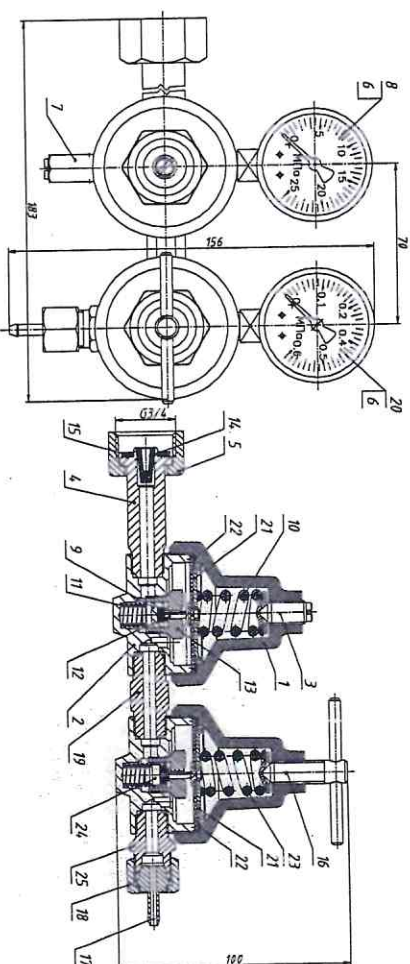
Редуктор баллонный газовый двухступенчатый.
